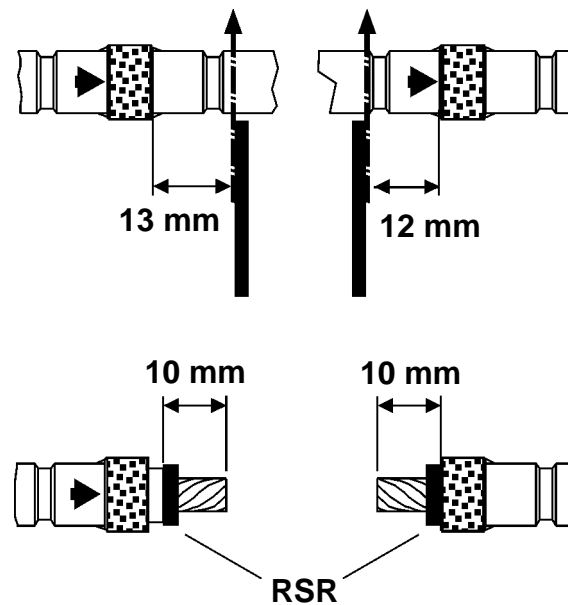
Corte del hilo de diamante para acoplamiento atornillable
